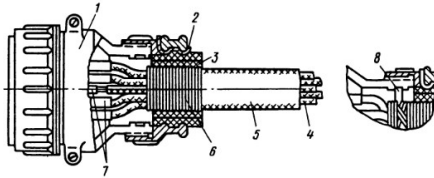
Заделка жгутов в ШР: 1 — ШР; 2, 3 — резиновые прокладки толщиной 1,5 и 2 мм; 4 — монтажные провода, образующие жгут; 5 — резиновая трубка; 6 — бандажные нитки; 7 — припой; 8 — стопорное кольцо
